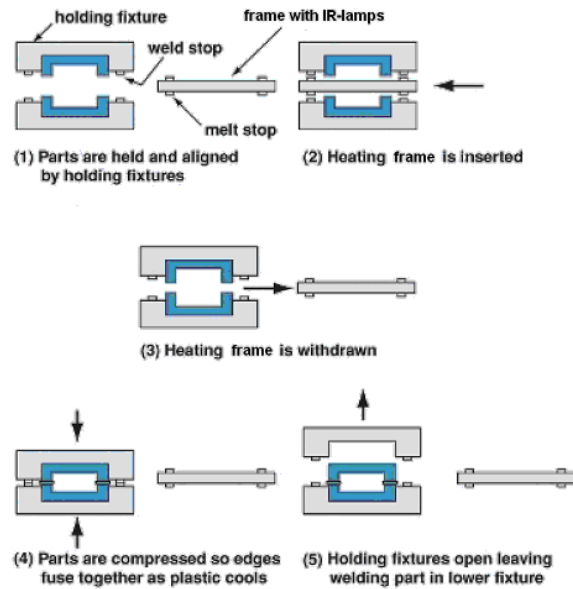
Rappresentazione schematica del processo "infrared welding"
